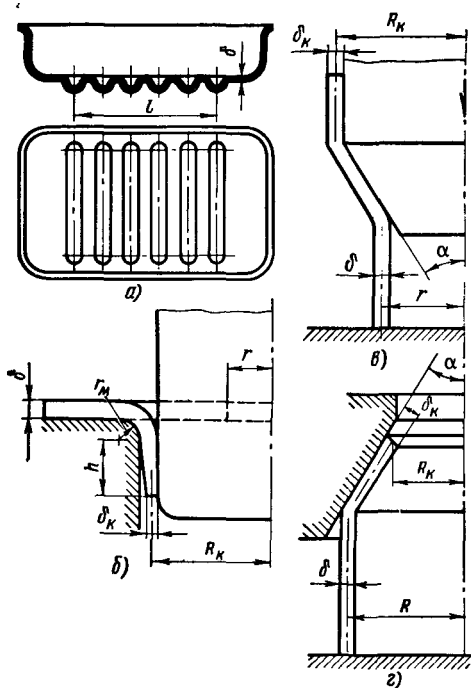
Схемы прессов и примеры рельефной формовки (а), отбортовки круглого отверстия (б), раздачи трубчатой заготовки коническим пуансоном (в) и обжима конической матрицей (г)
